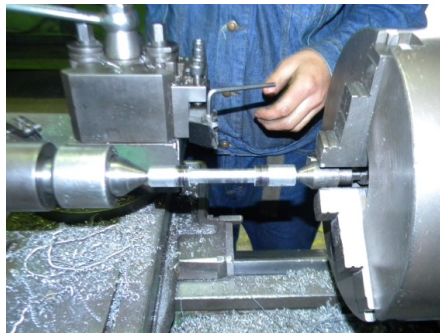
Maquinado de las probetas según especificaciones ASTM E8:04 especimen 01
